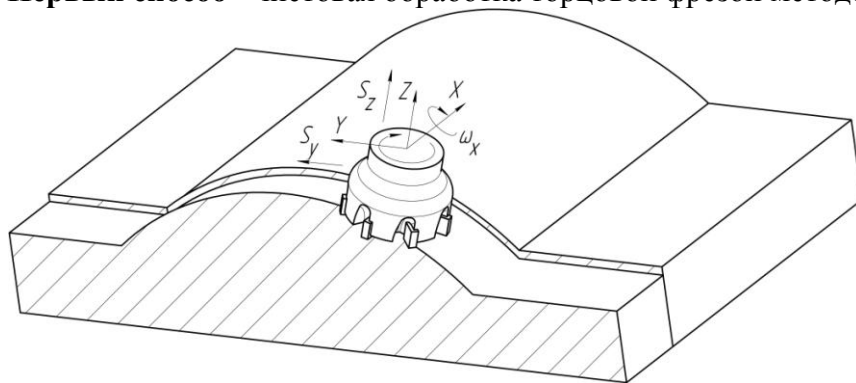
Схема обработки торцевой фрезой методом обката
